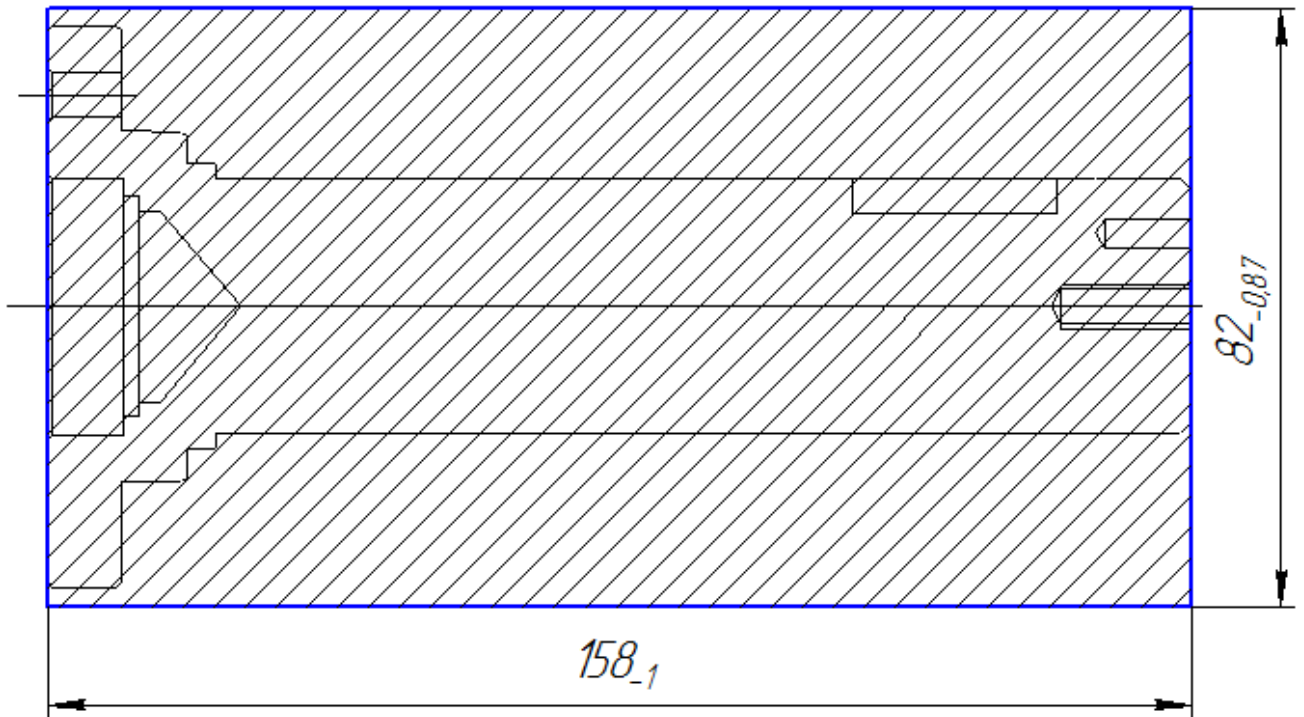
Ескіз заготовки отриманої з прокат розрізаного різцем
